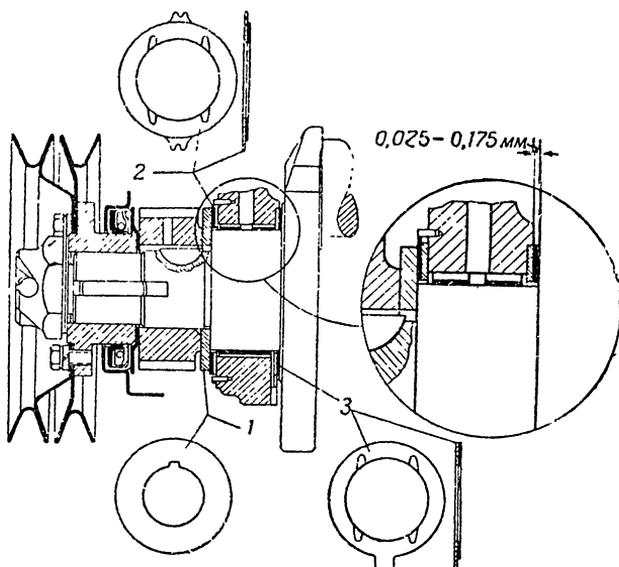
Передний подшипник коленчатого вала с упорными шайбами:
